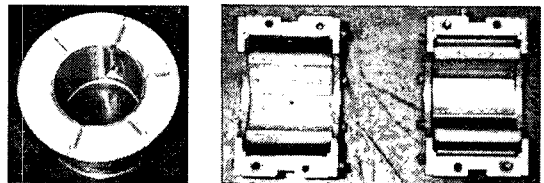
Journal Bearing과 Tilting-Pad Bearing
